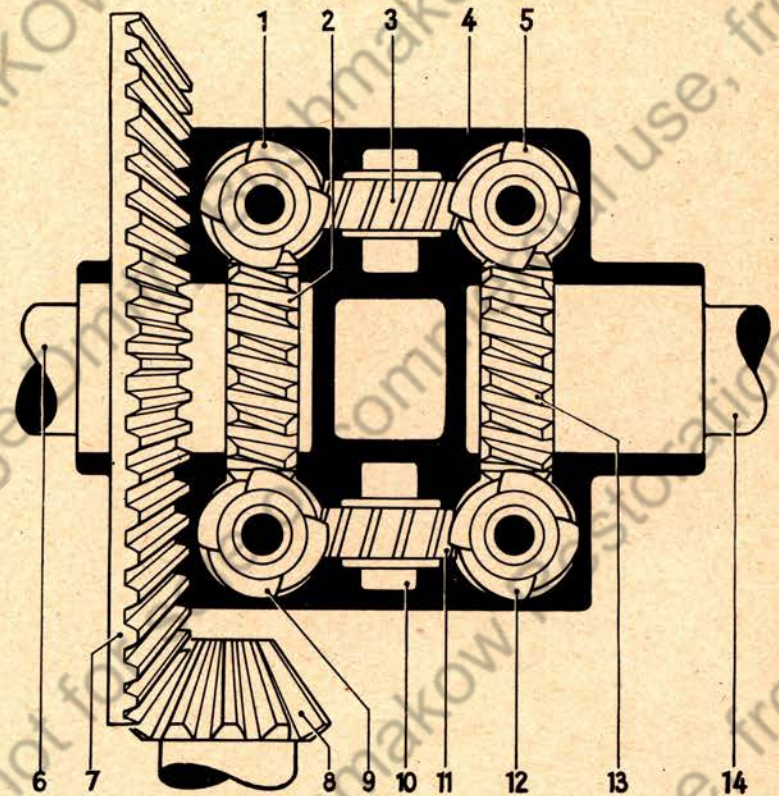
Schneckenrad-Ausgleichgetriebe (Schema)
